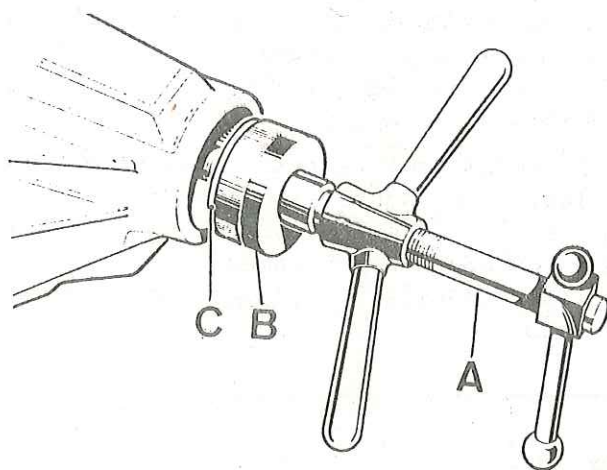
Montaje de la pista del cojinete del extremo de la brida
